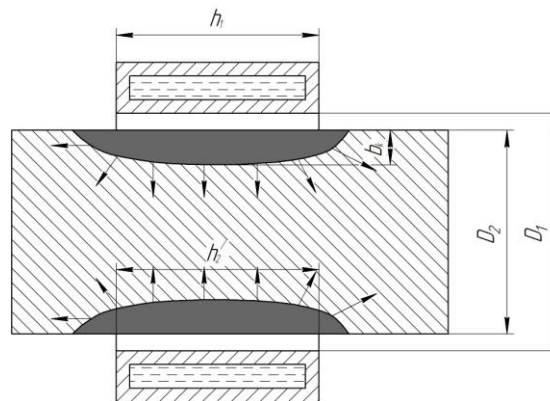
Система індуктор-деталь установки одночасного нагріву
